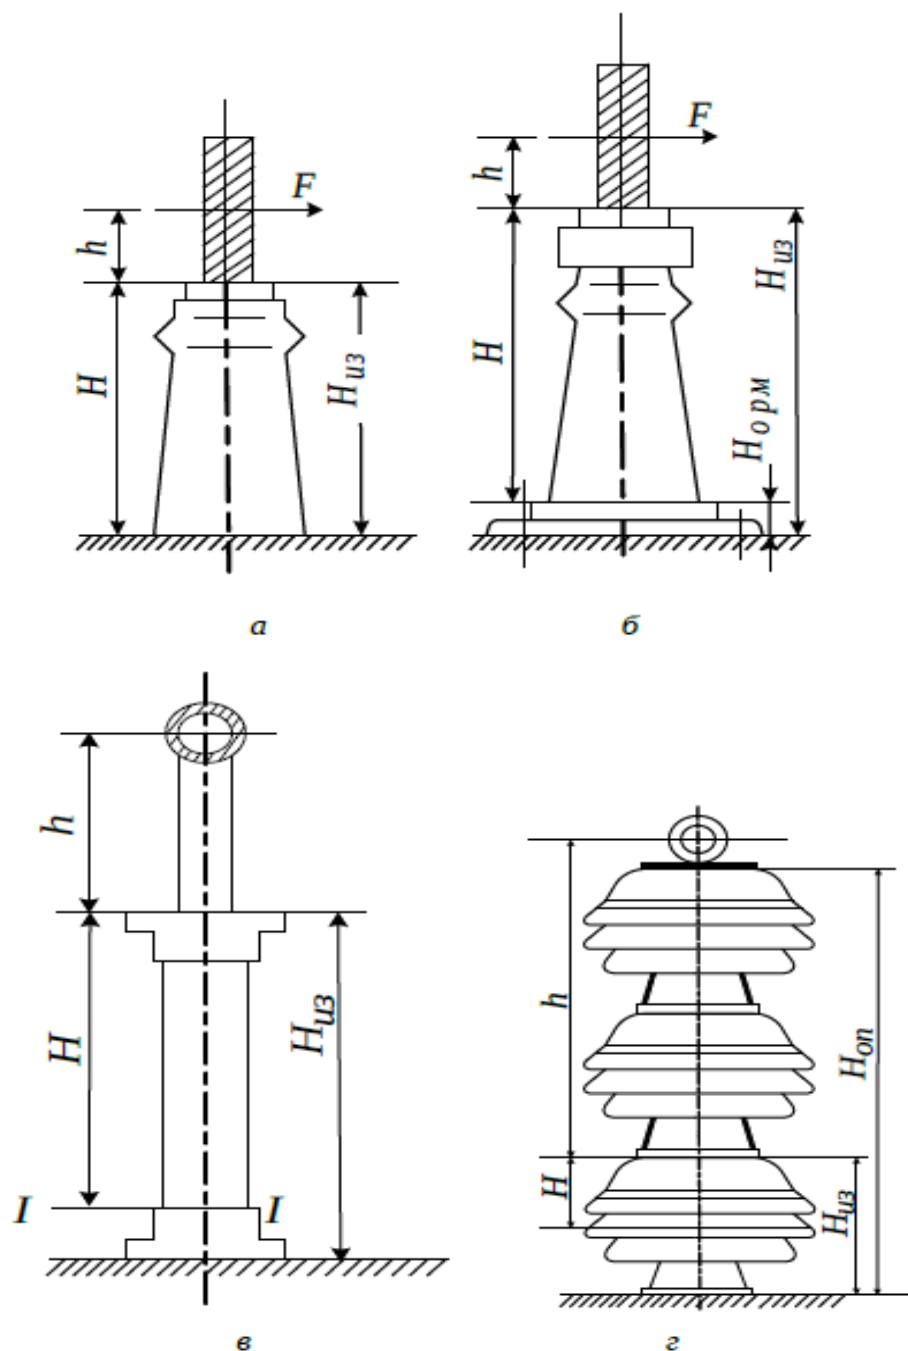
К определению допустимых нагрузок на изоляторы
